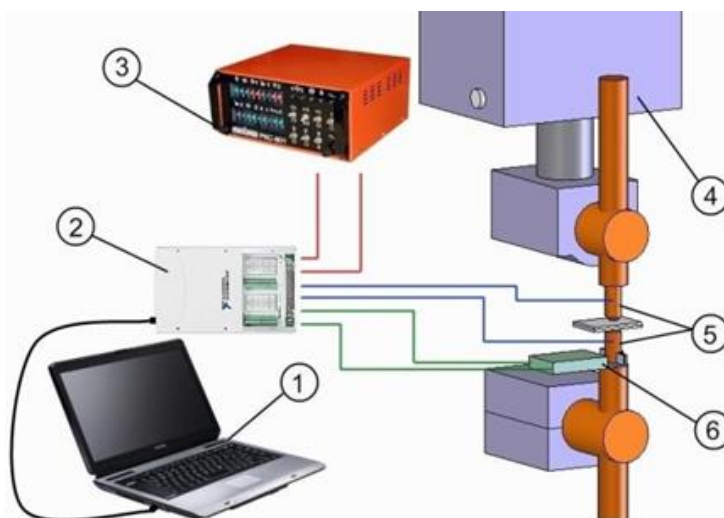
Установка для автоматического управления процессом контактной точечной сварки: 1 – ЭВМ; 2 – универсальное устройство сбора данных National Instruments USB-6251; 3 – регулятор цикла сварки РКС-801; 4 – машина для контактной сварки МТ-3201; 5 – датчик напряжения электрод-электрод; 6 – датчик тока с источником питания
